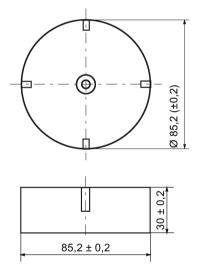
Desenho de dimensões do espaçador 6GT2690-0AA00
